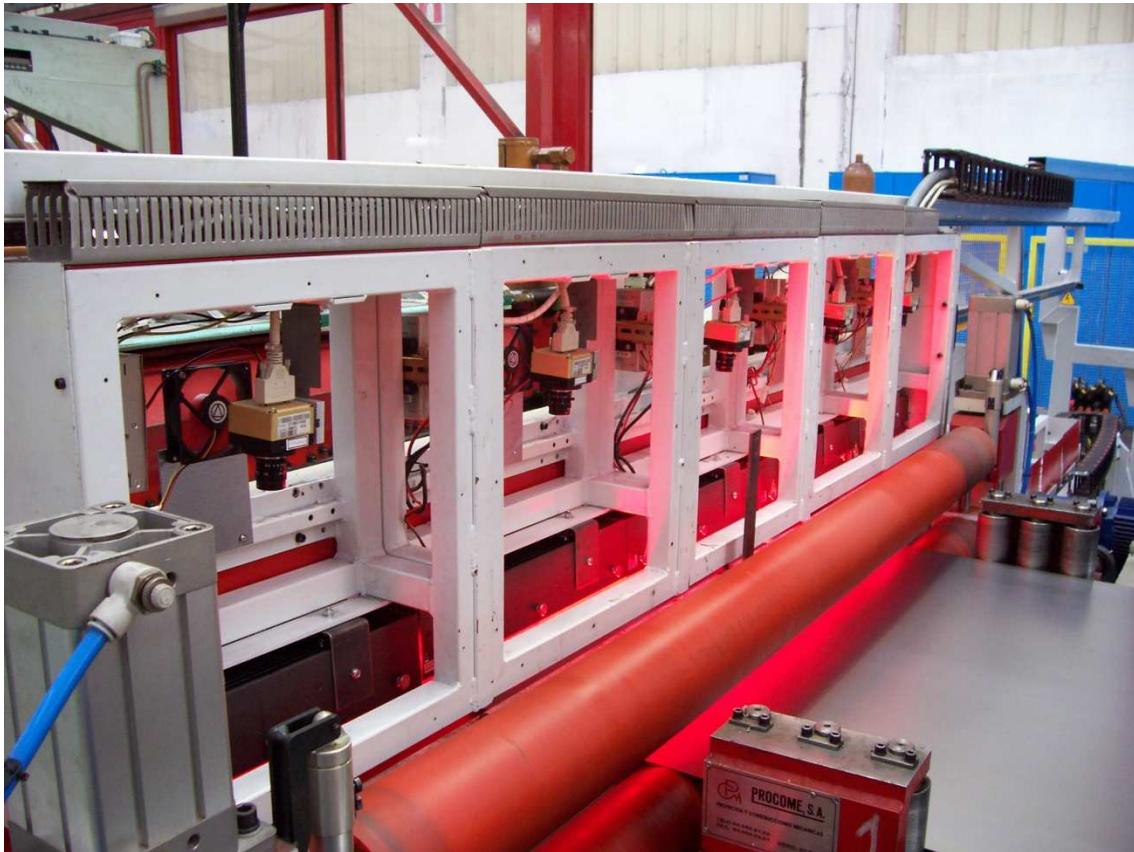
Módulos de la cara superior del sistema de inspección de chapa laminada. Cada módulo dispone de cámara e iluminación. Las cubiertas para aislar el sistema de la iluminación ambiente han sido retiradas.
